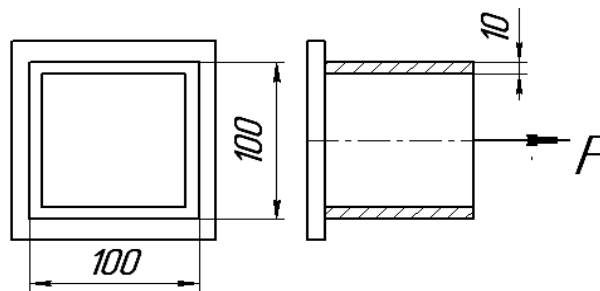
Сварное соединение, выполненное тавровыми сварными швами
